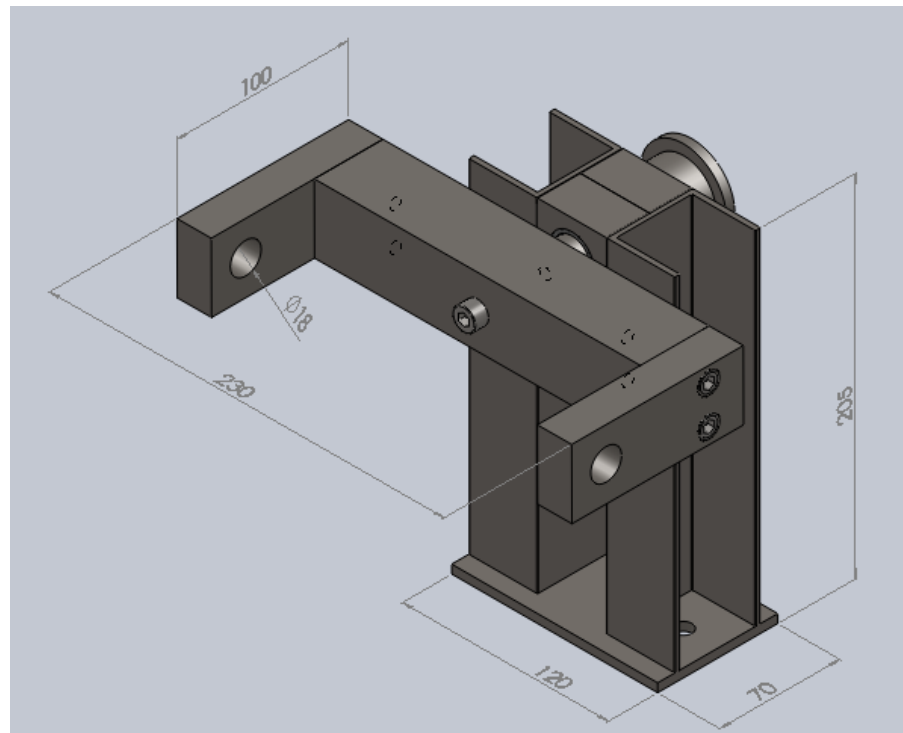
13. Soporte delantero potro de soldadura
